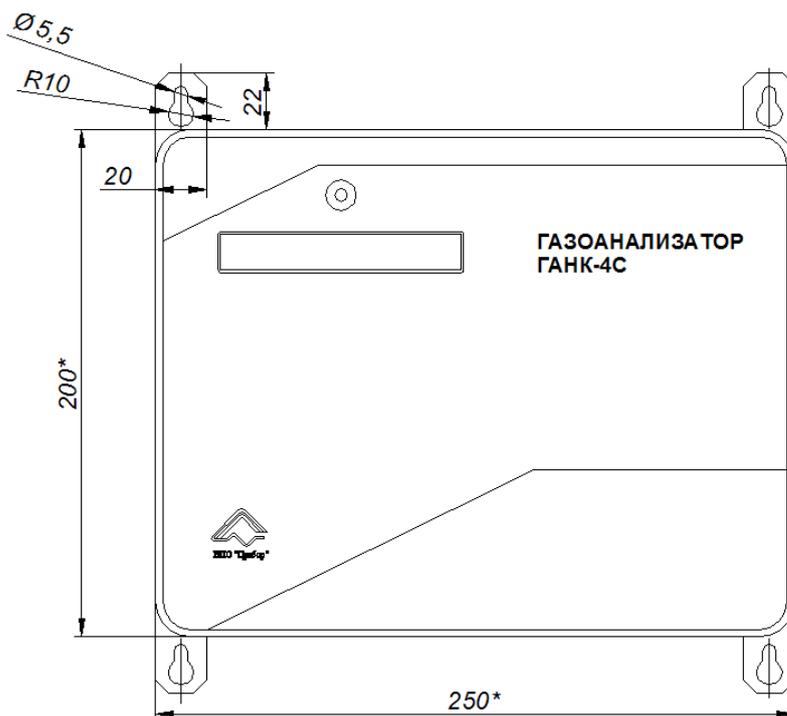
Размеры для установки газоанализатора ГАНК-4С
